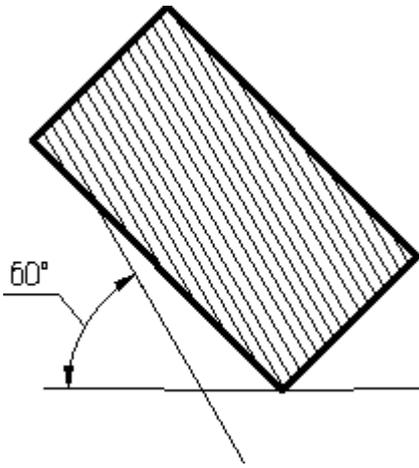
Штриховка под углом 60° к рамке чертежа
